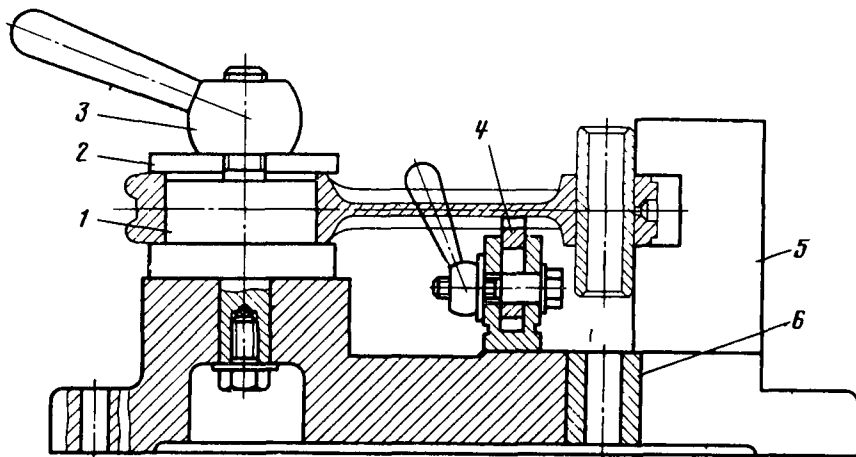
Приспособление для контроля и рихтовки шатунов:
